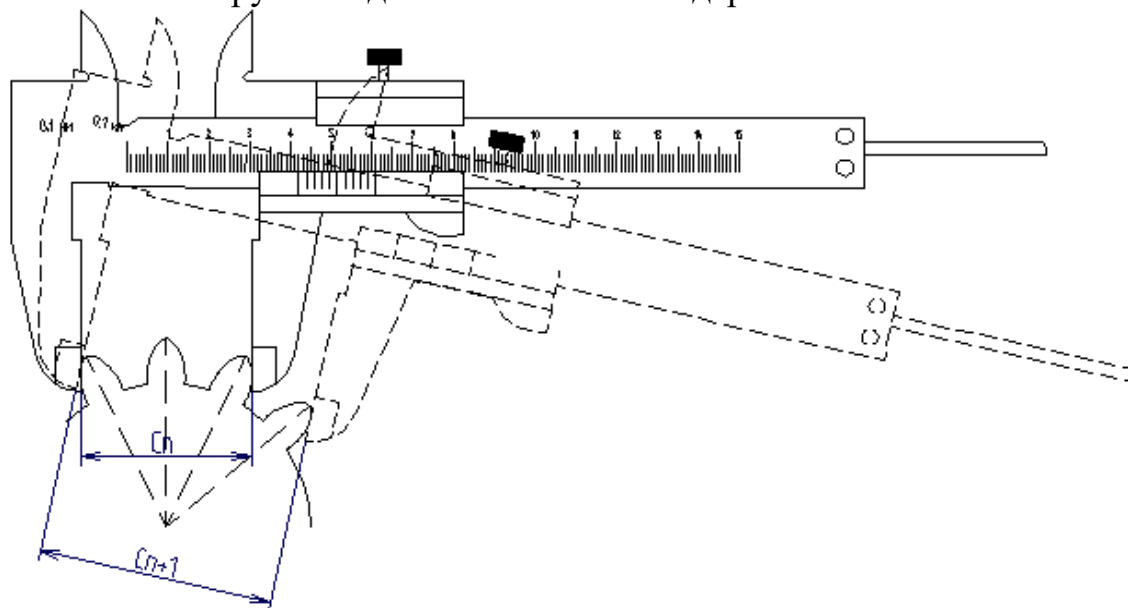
Схема измерения зубчатого колеса штангенциркулем.
